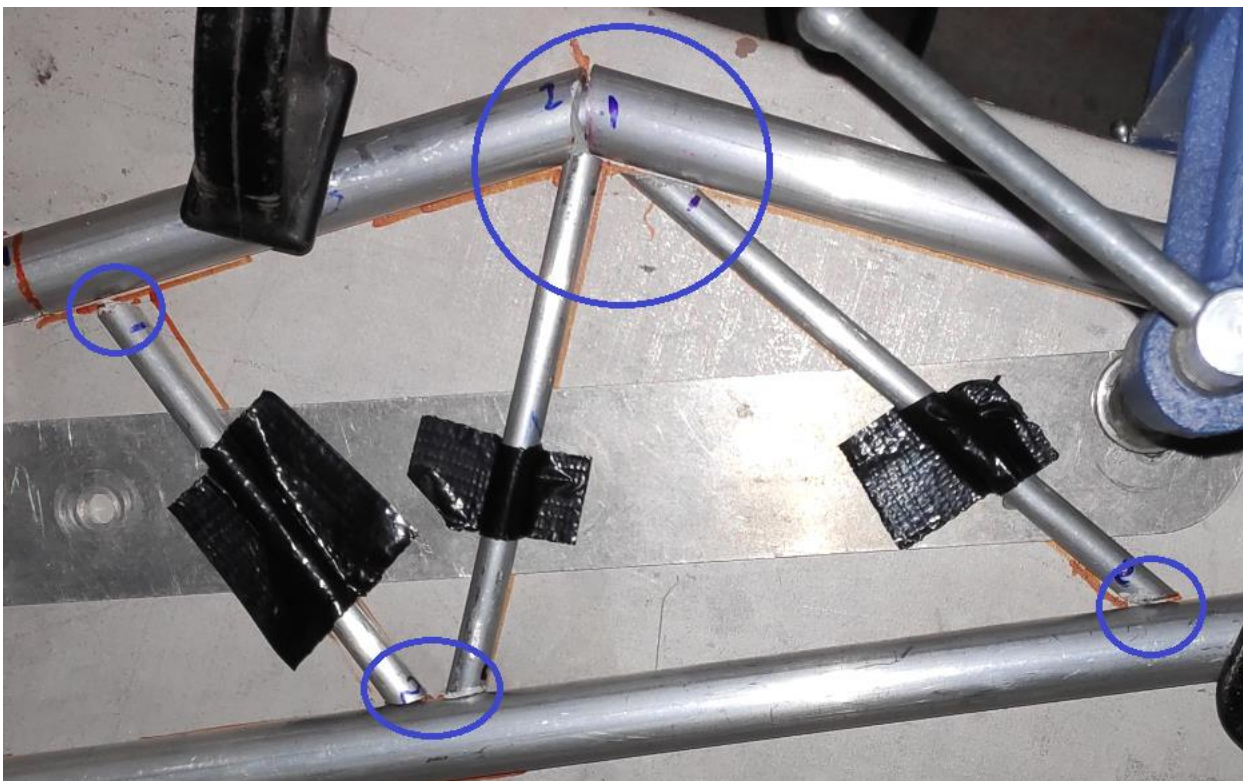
Detalle de la separación entre elementos previo a la soldadura
